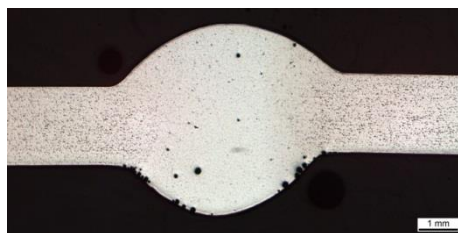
Микрошлиф сварного шва, выполненного проволокой диаметром 1,2 мм
